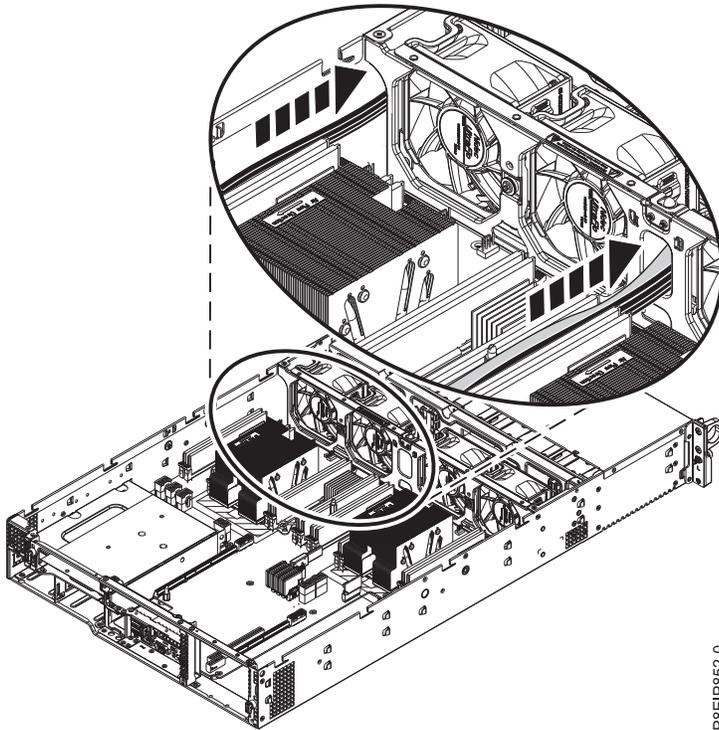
Kabel der Rückwandplatine des Laufwerks entfernen
